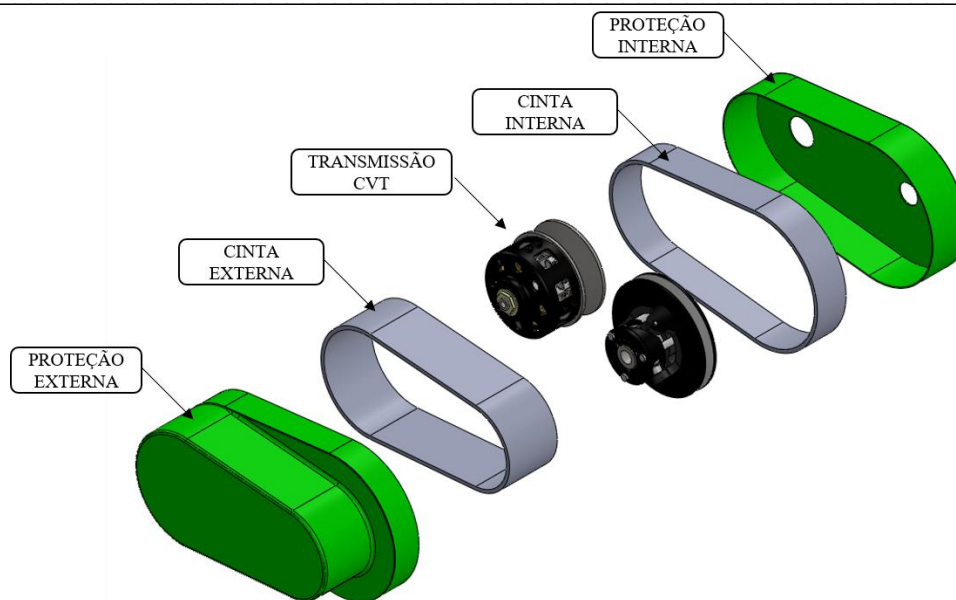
Vista explodida da montagem da proteção de CVT. (Autoria própria)
